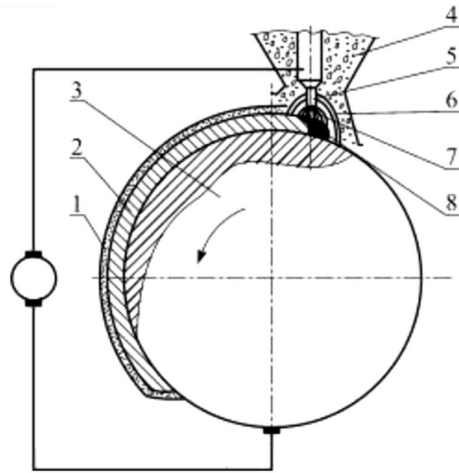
Схема наплавлення під шаром флюсу: 1 – шлакова кірка; 2 – наплавлений шар; 3 – деталь; 4 – флюс; 5 – електродний дріт; 6 – еластична оболонка; 7 – електрична дуга; 8 – ванночка з розплавленим металом [2, с.98]
